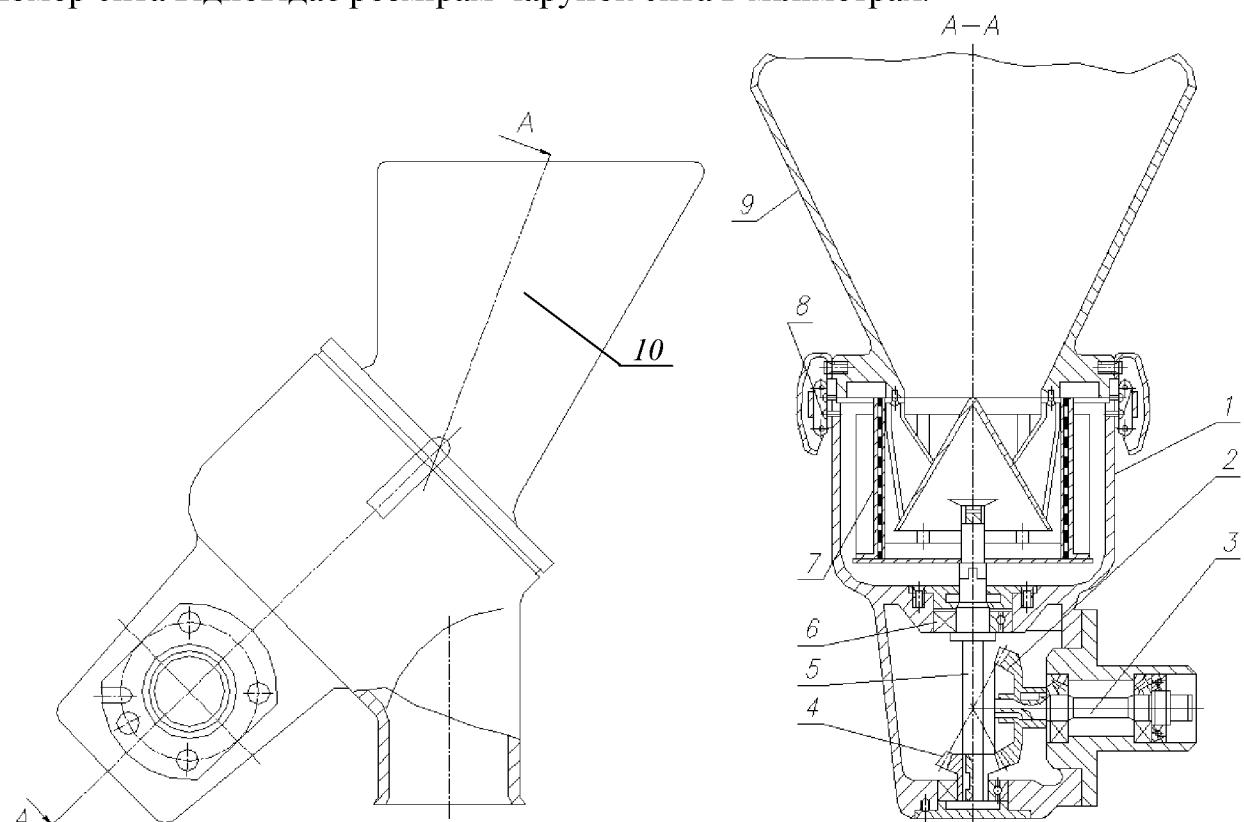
Просіювач МПП-ІІ-І: 1 – корпус; 2 – колесо конічне; 3 – вал привідний; 4 – шестерня зубчаста; 5 – вал робочий; 6 – опори качення; 7 – барабан-сито; 8 – засувки; 9 – лійка завантажувальна; 10 – патрубок розвантажувальний
